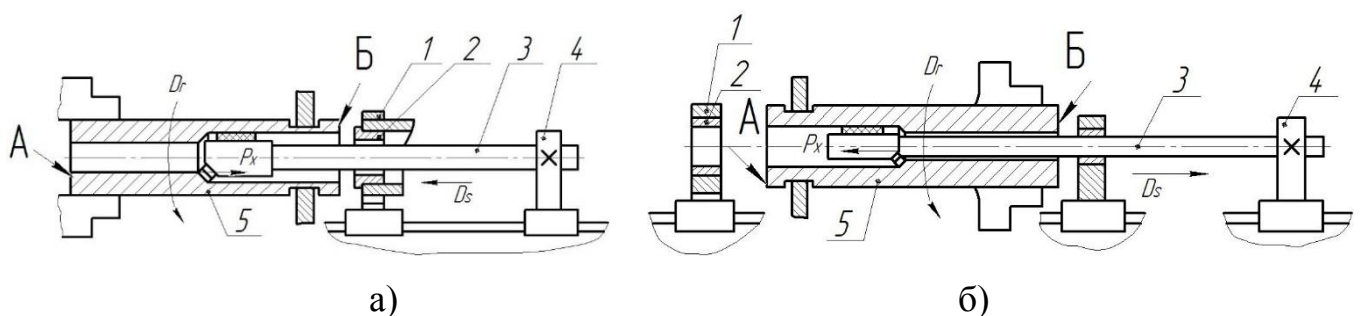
Схеми оброблення глибоких отворів циліндрів: а) оброблення «на стиск»; б) оброблення «на розтяг».
